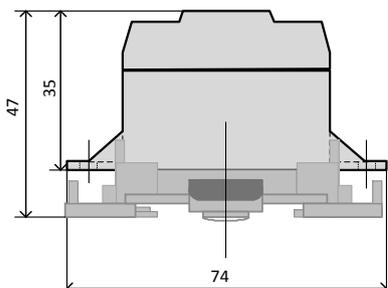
Габаритные размеры устройства для монтажа на рейку DIN.
